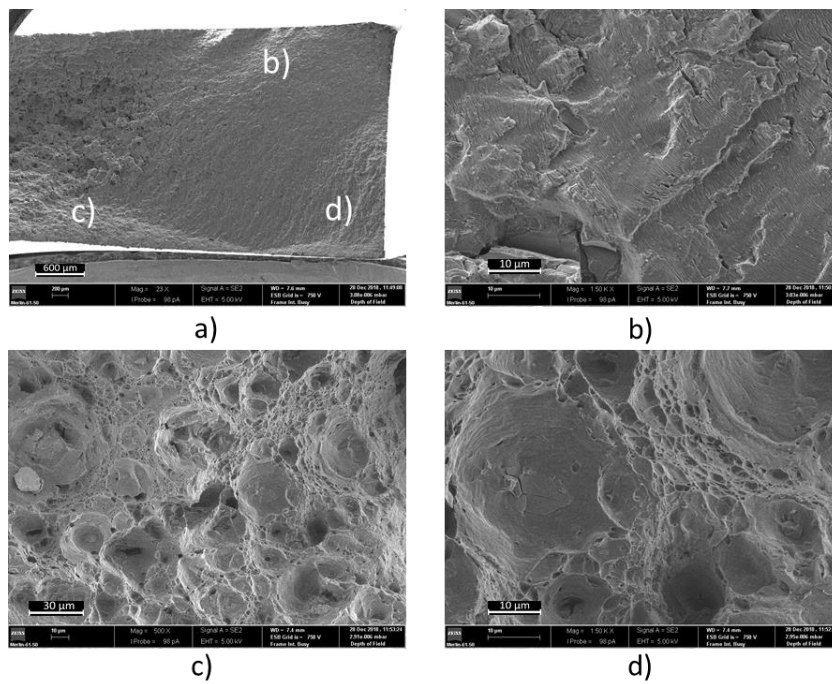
Fratografia das superfícies de fratura do provete 562-60-F-5: a) vista geral da superfície de fratura; b) zona de propagação por fadiga da fratura; c) zona de rotura final do provete; d) zona de rotura final do provete.
